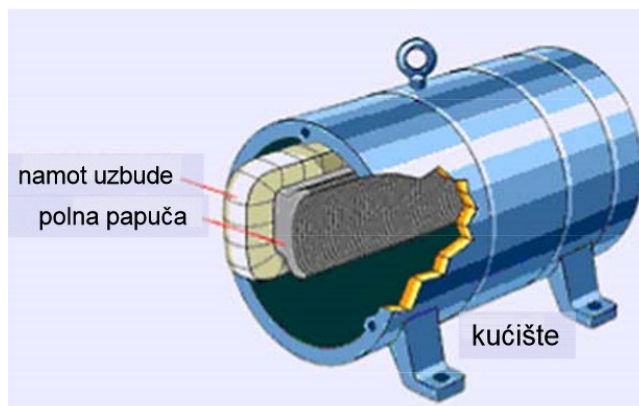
Istosmjerni motor "GE 752 High-Torque DC drilling motor"
